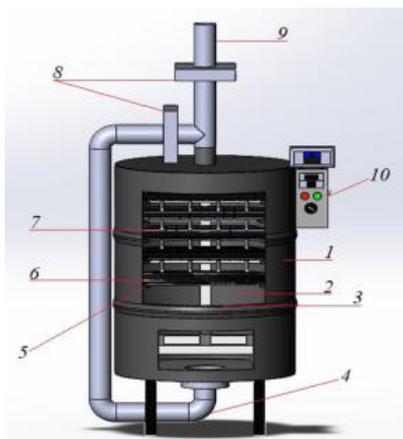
Экспериментальная установка процесса сушки плодов томатов: 1- корпус; 2-отражатель; 3-изоляционный слой; 4-потрубок для приёма воздуха; 5-механизм для передвижения сетчатого поддона; 6-сеточный поддон; 7-блок излучателей; 8-шибер; 9-патрубок для удаления влажного воздуха; 10-пульт управления.
